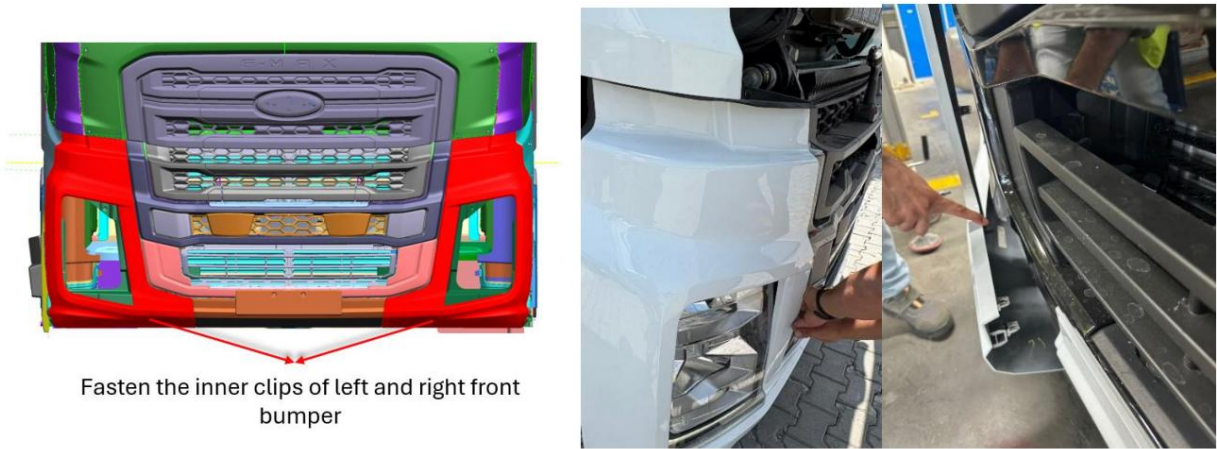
Installation des pièces du carénage du pare-chocs avant gauche et droit.
